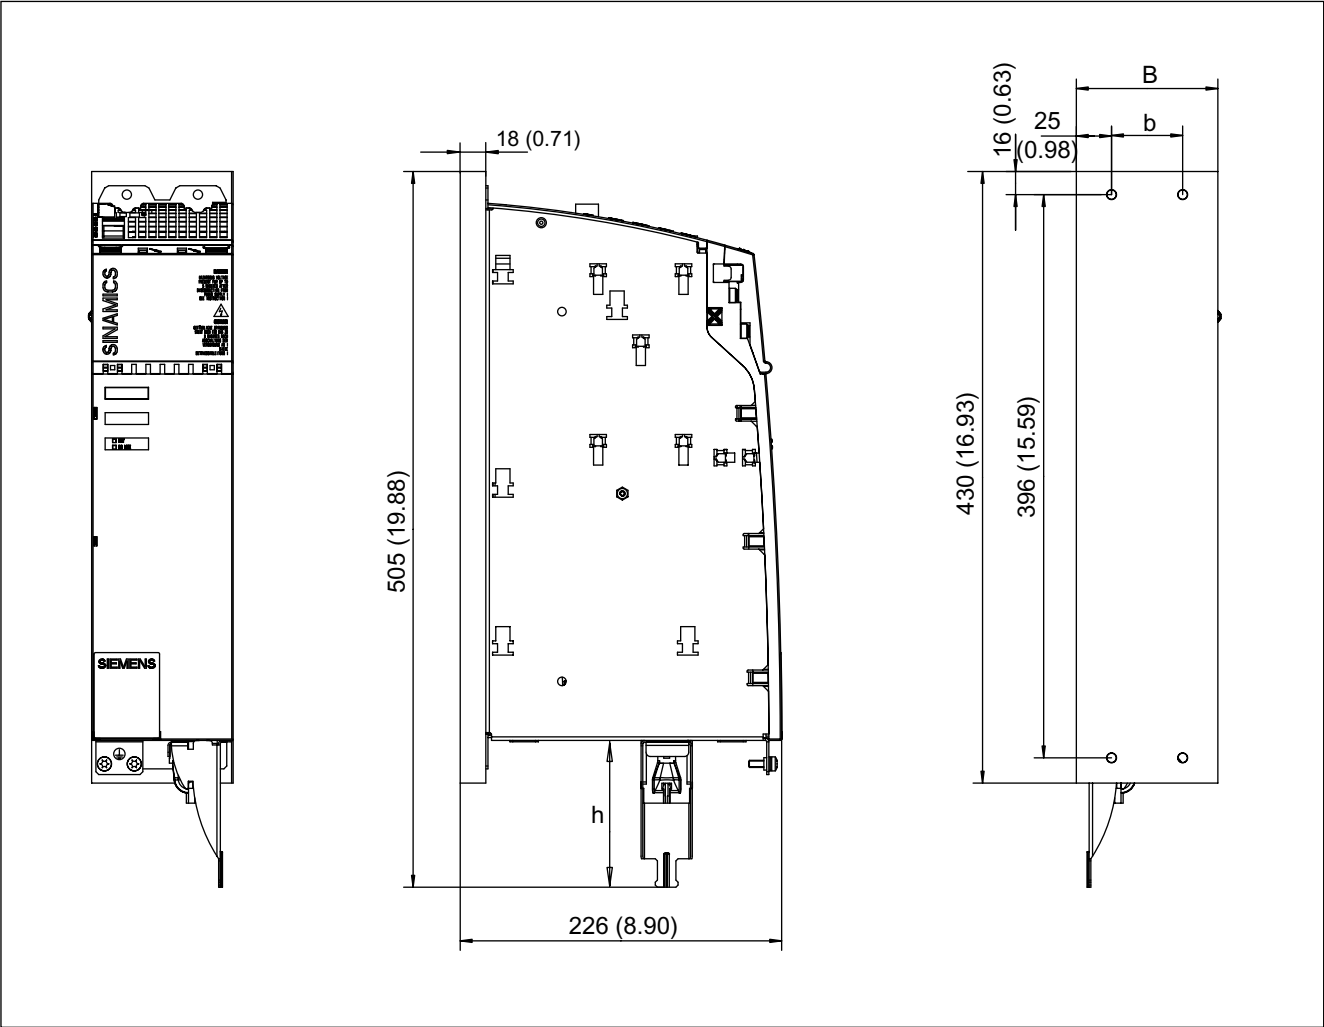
Disegno quotato Motor Module con Cold-Plate 18 A e 30 A
